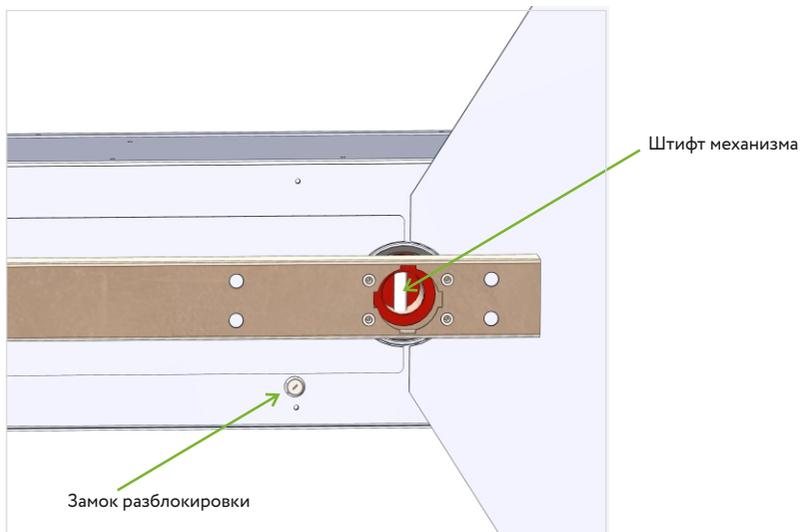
Место установки верхнего подшипникового узла (вид снизу)
